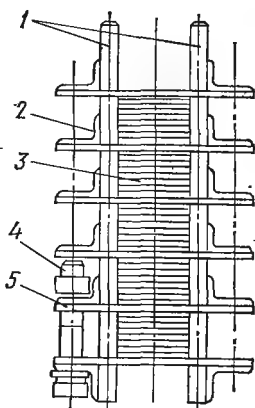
Приспособление для прессовки прокладок и реек из электрокартона: 1 — стальные стержни, 2 — угольник, 3 — прессуемые детали, 4 — болт с гайкой, 5 — прижимная стальная планка
